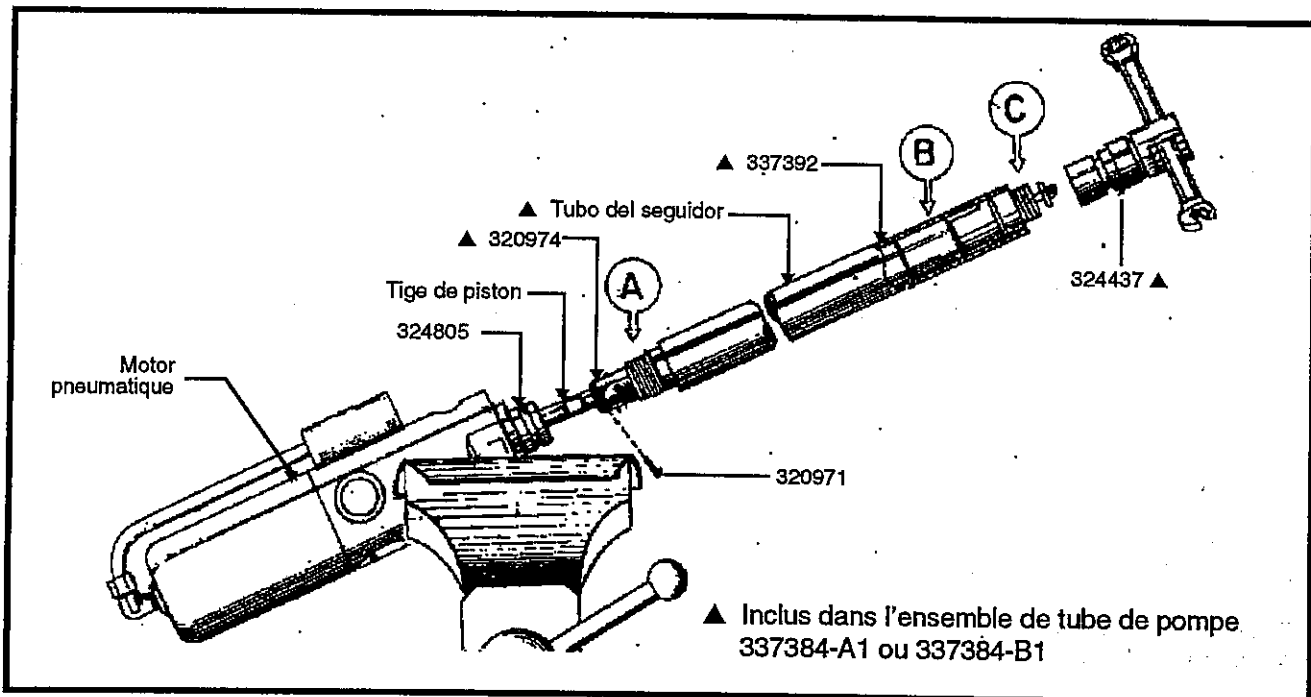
Dégagement du moteur pneumatique de l'ensemble de tube 337384-A1 ou 337384-B1
